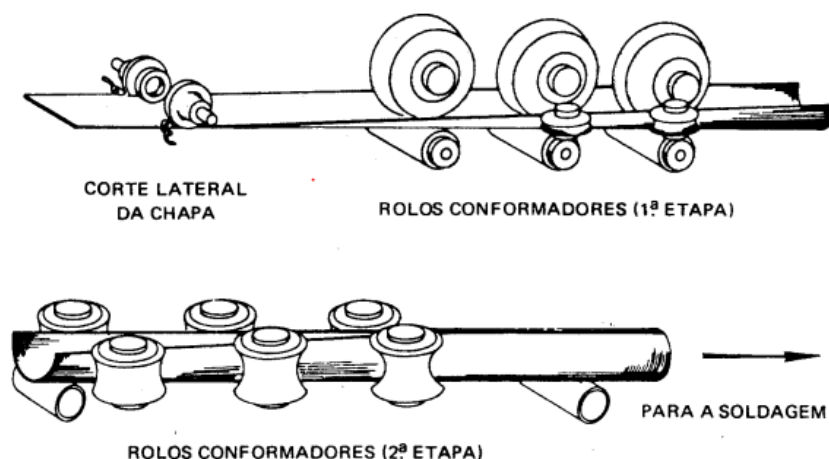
Fabricação de tubos a partir de bobinas de chapa.
